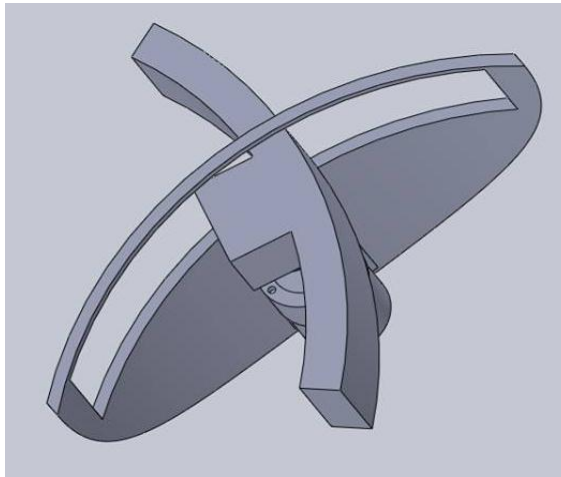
Mecanismo para patear la pelota diseñado en SolidWorks
